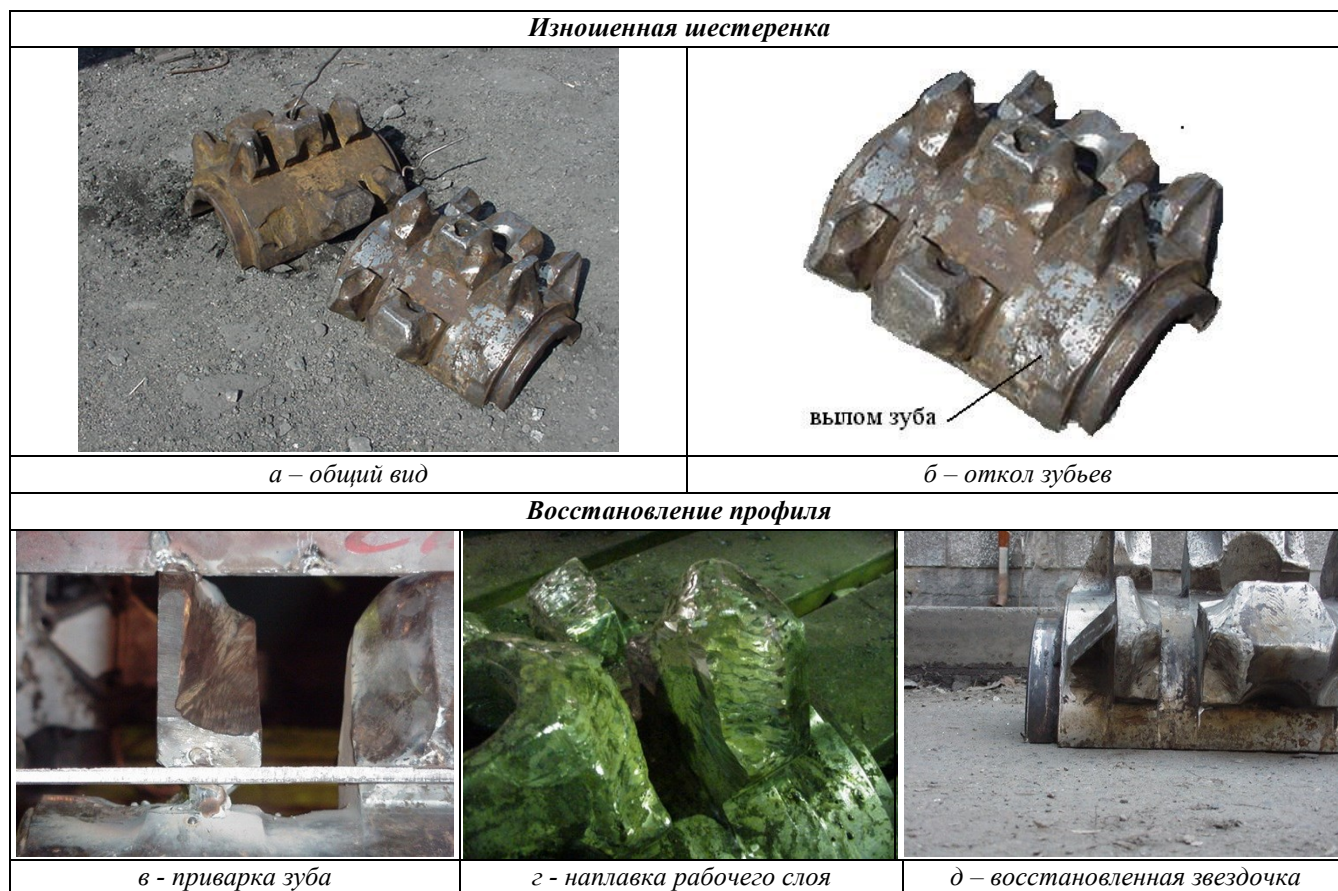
Общий вид (а), откол зубьев (б) изношенной шестеренки и восстановление профиля (приварка зуба (в), наплавка рабочего слоя (г), восстановленная звездочка (д))
